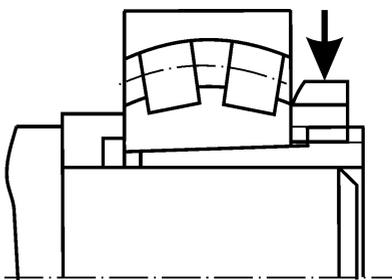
Разборка подшипников со стяжной втулкой с помощью шлицевой гайки и накидного ключа
